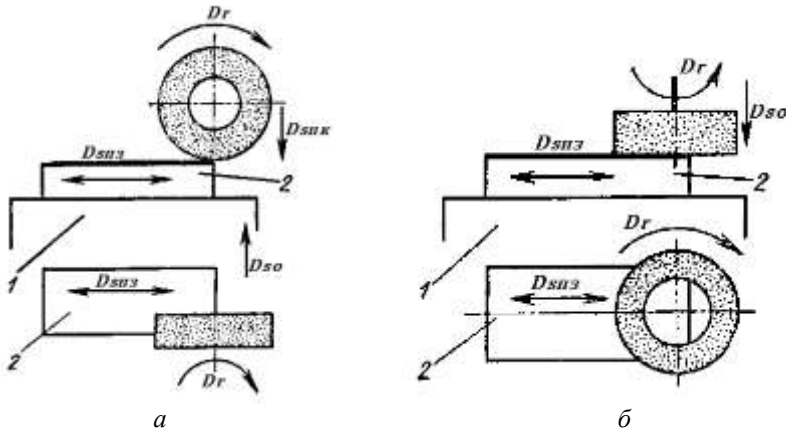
Схеми плоского шліфування. 1 – стіл; 2 – заготовка
